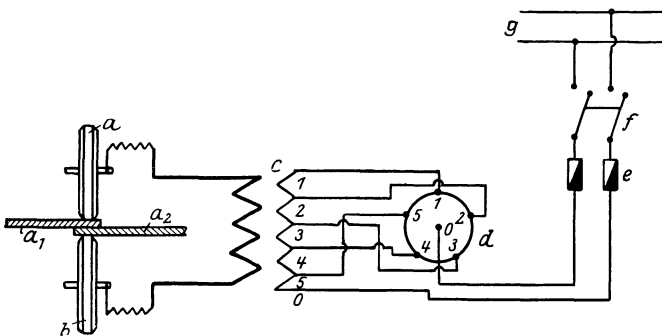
Schaltung und Stromzuführung bei Nahtschweißmaschinen.
